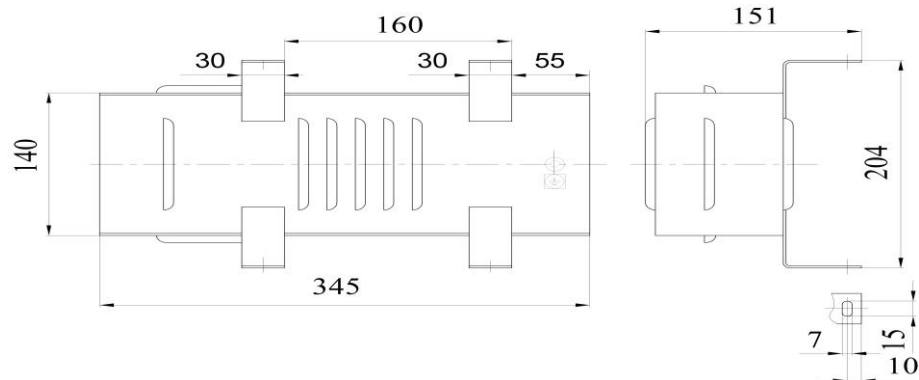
Габаритный чертеж ПЭТ-11-04
